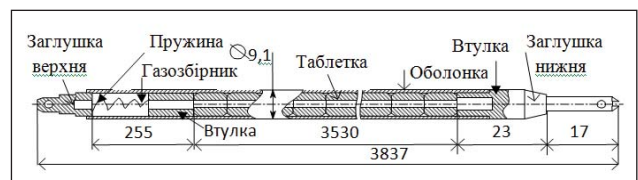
Конструкція та габаритні розміри ТВЕЛа
